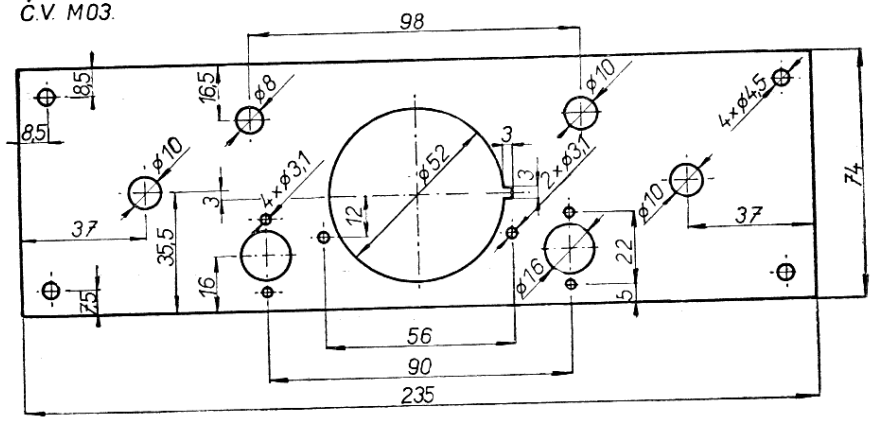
M16. Výkresy mechanických součástí přístroje
